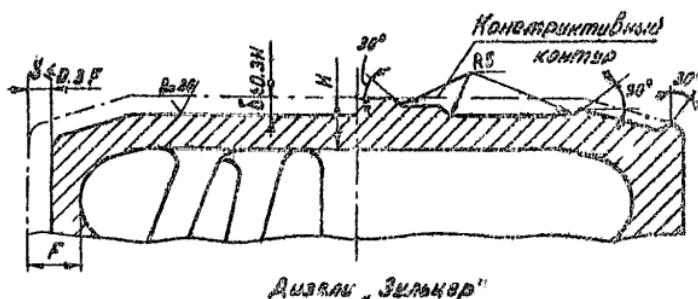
Подготовка днища и наружной цилиндрической поверхности головки поршня к восстановлению
